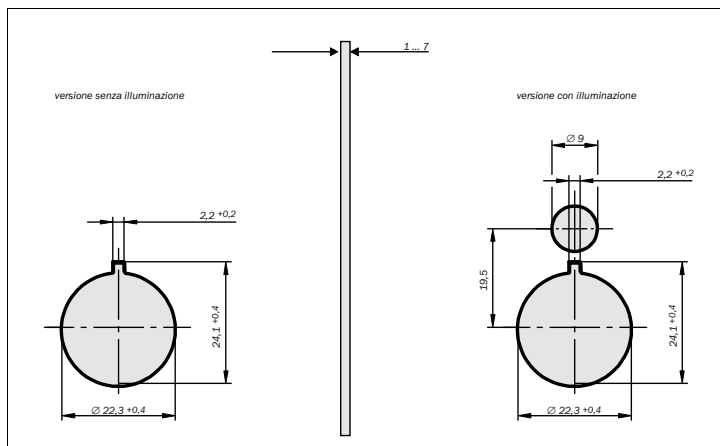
disegni quotati dei fori di montaggio per le versioni a incasso (mm)
